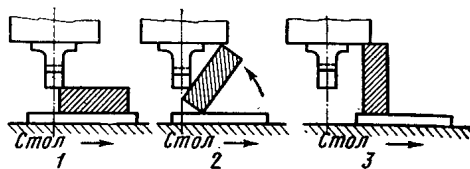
Схема поворота заготовки в вертикальное положение при помощи передвижного стола и траверсы пресса
